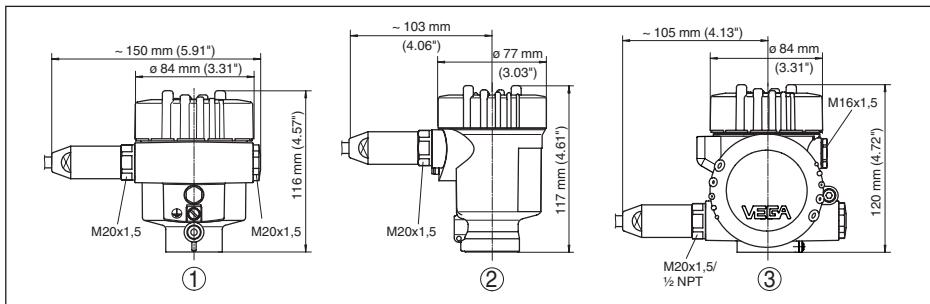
Корпус в исполнении IP 66/IP 68 (1 bar) - с установленным модулем индикации и настройки корпус выше на 9 mm/0.35 in
